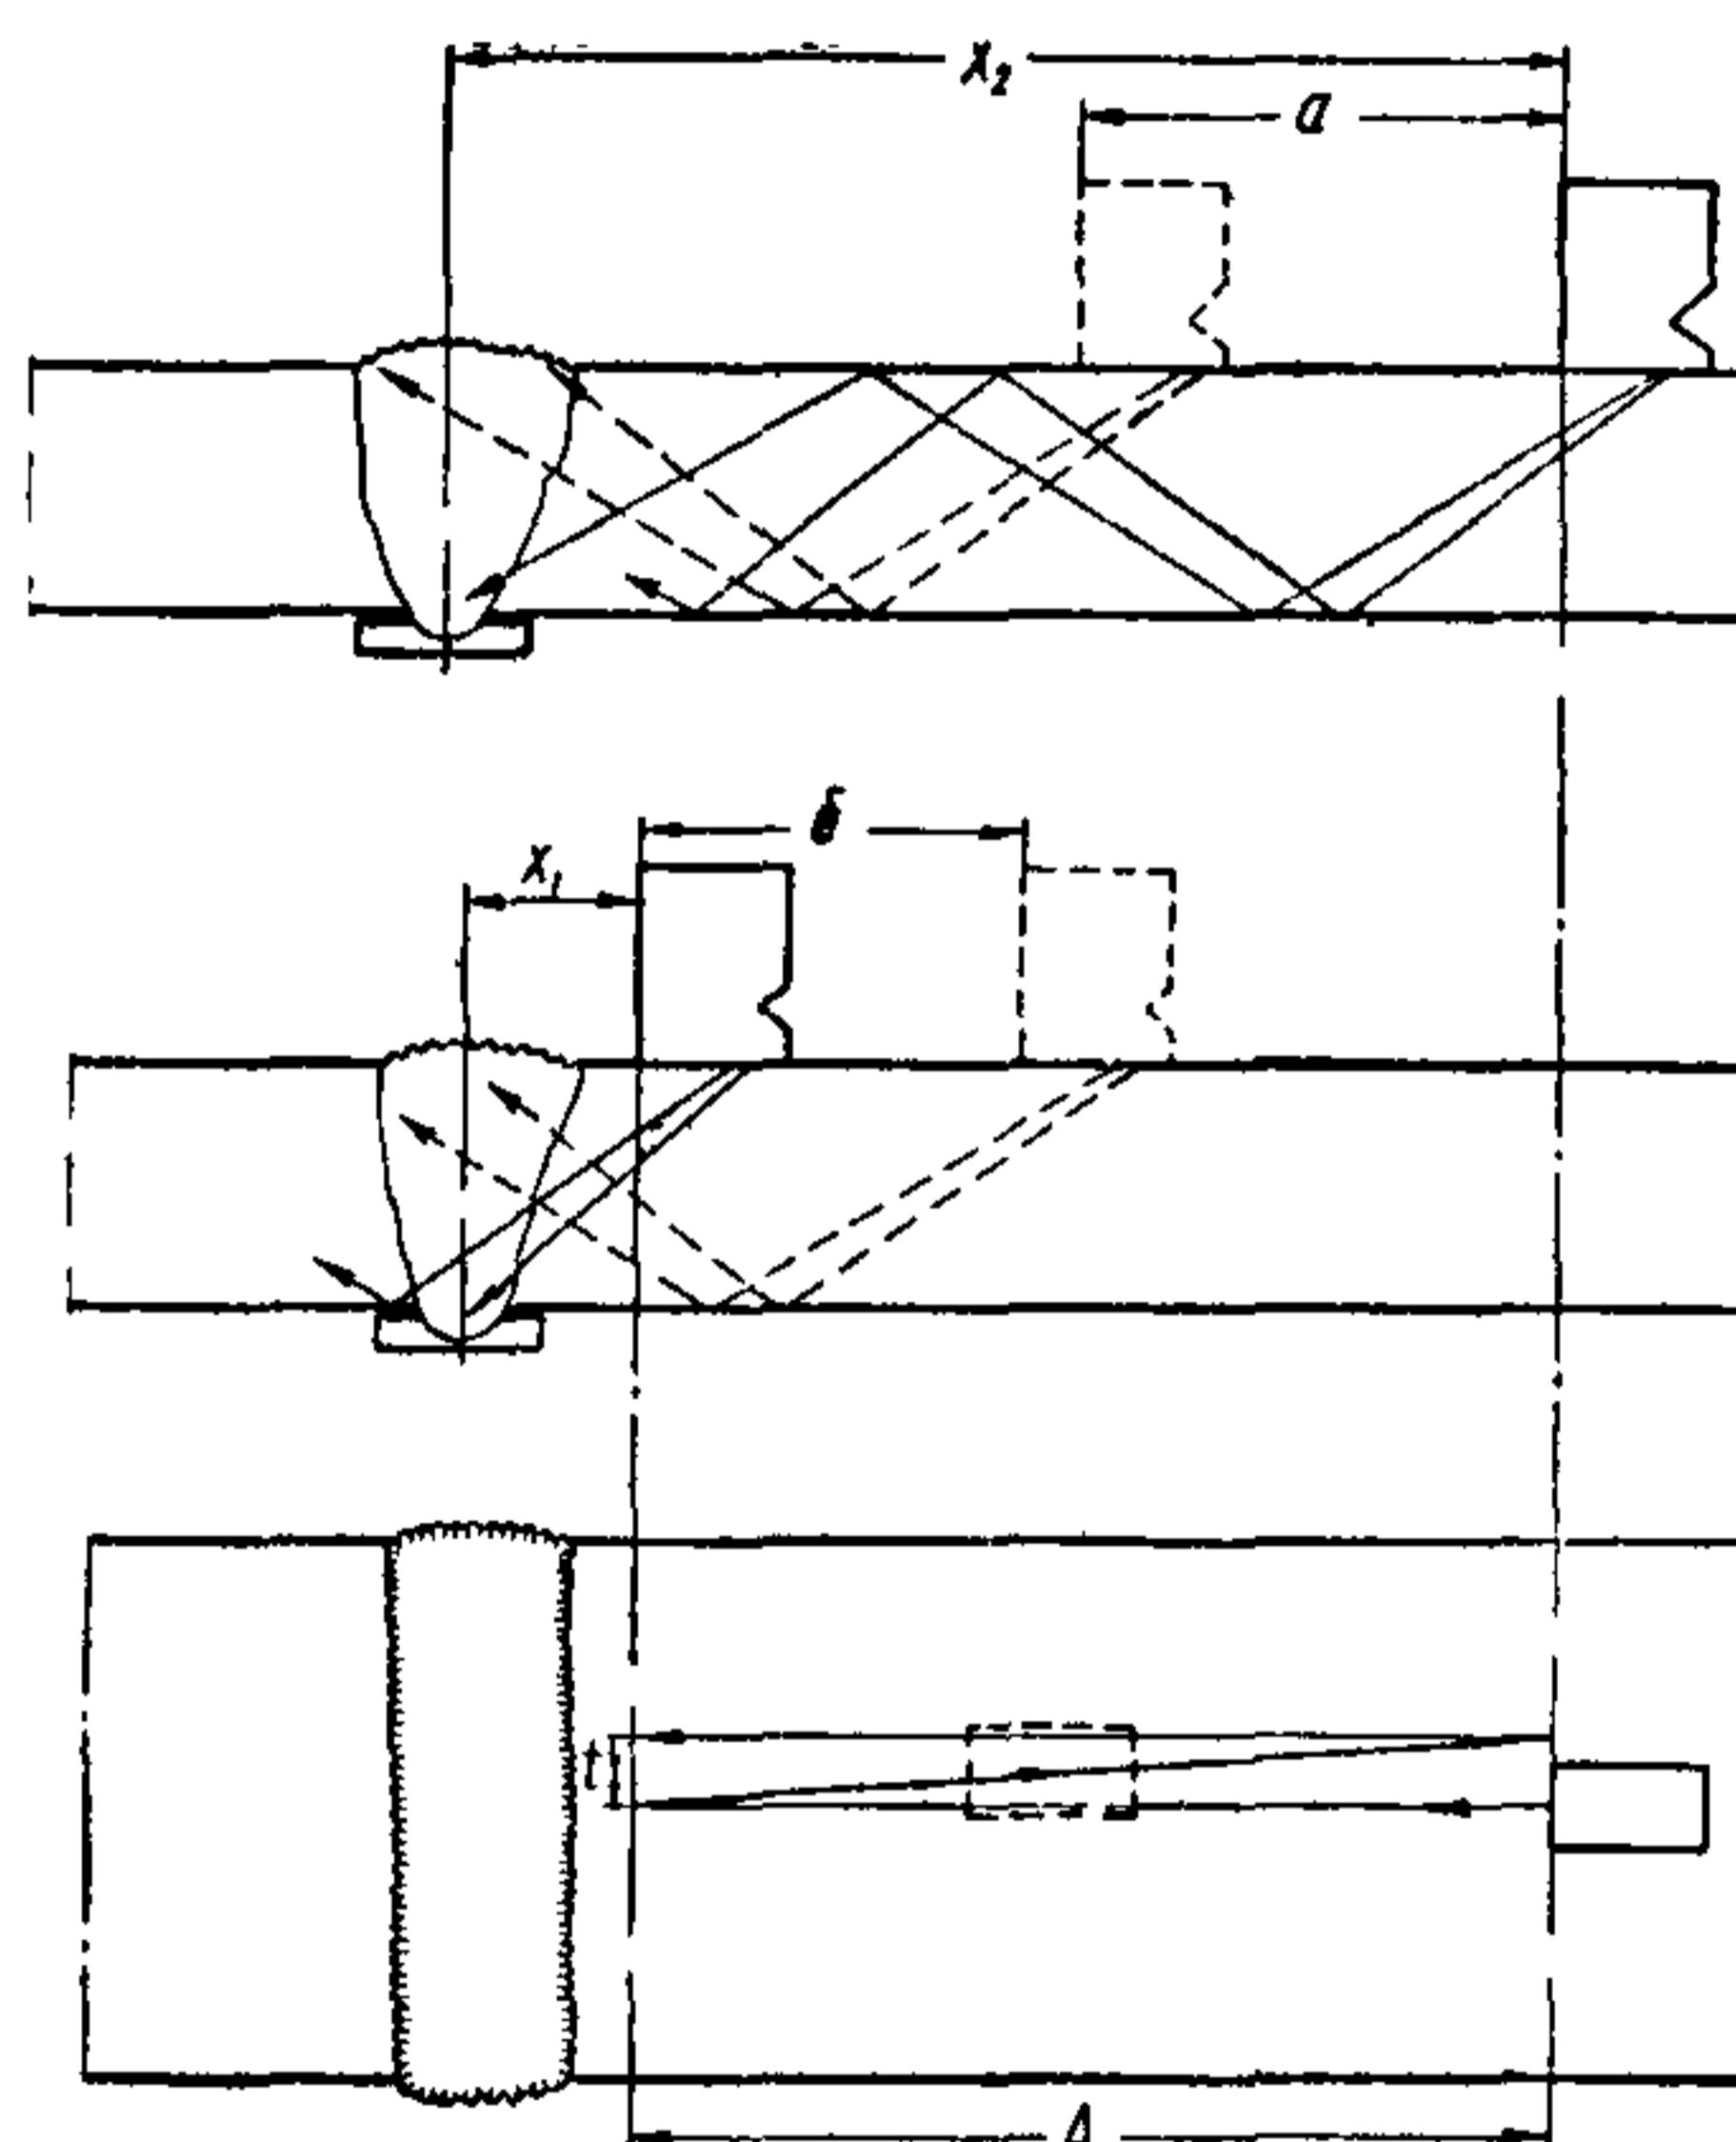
Перемещение щупа по поверхности трубы при контроле сварного стыка
